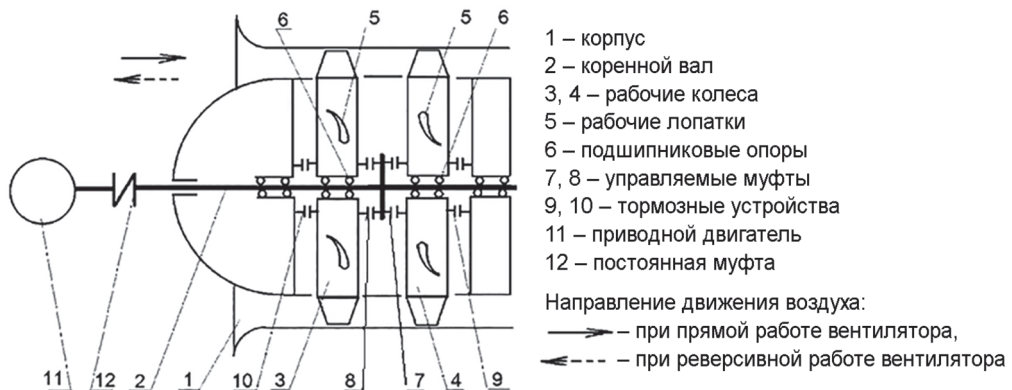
Кинематическая схема реверсивного осевого вентилятора с двумя рабочими колесами
